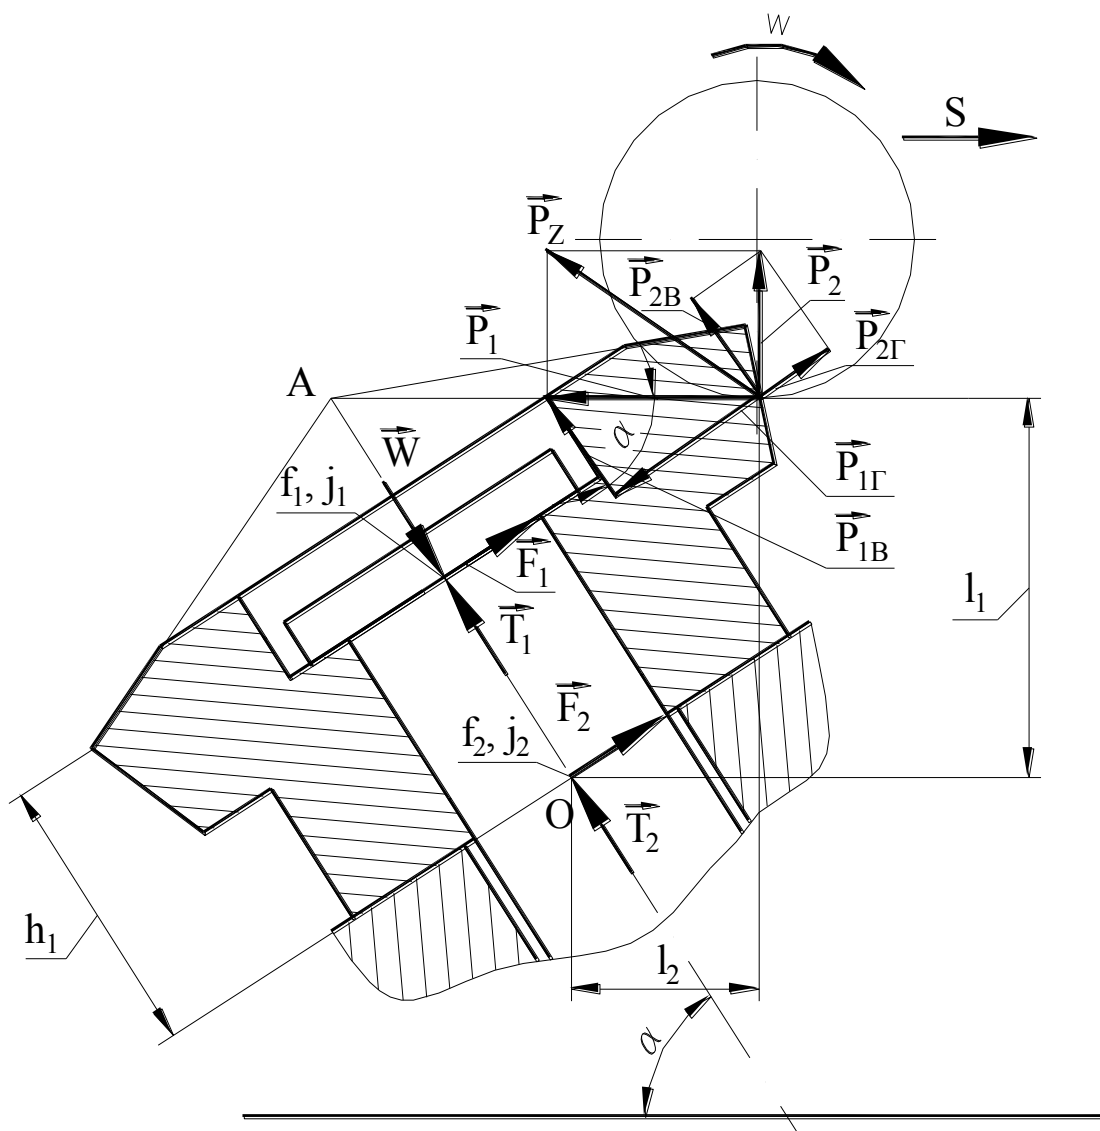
Схема сил, що діють на деталь під час фрезерування зуба
